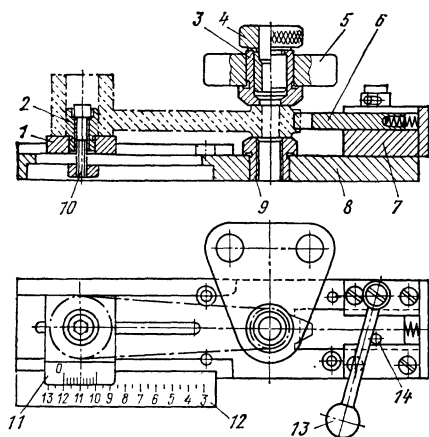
Переналаживаемый кондуктор для обработки второго отверстия в бобышке рычага
